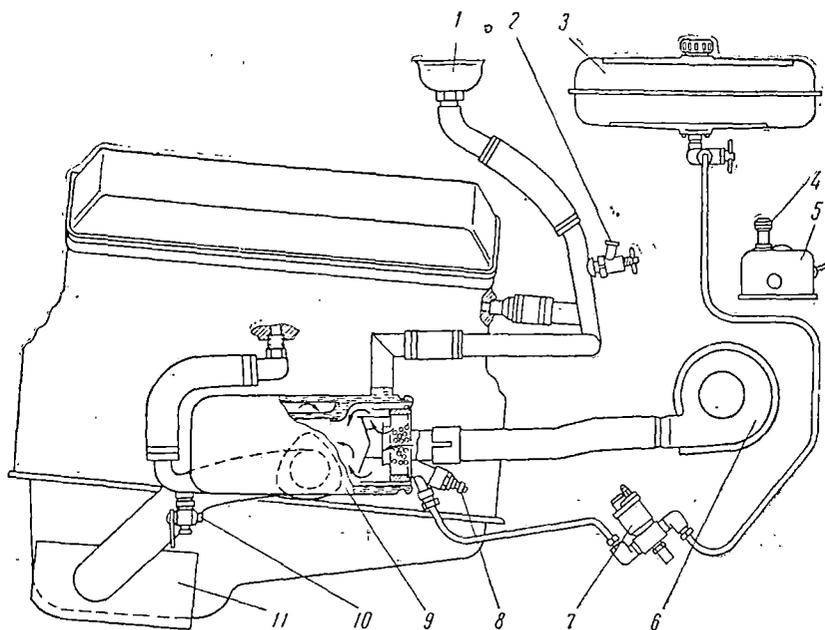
Пусковой подогреватель двигателя автомобиля ГАЗ-66:
